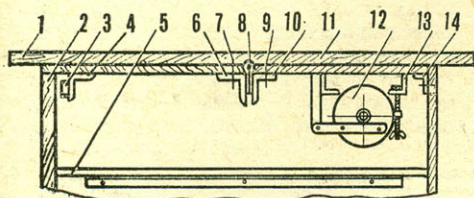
Разрез тумбочки закрытого стола (вид справа):
